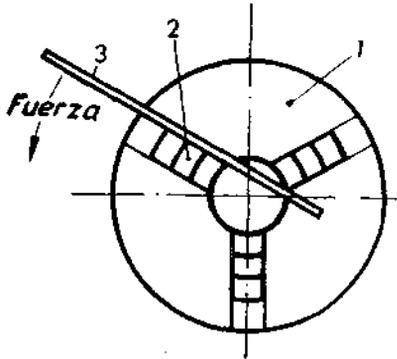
Desmontaje del plato universal. — 1, Plato. — 2, Patas. — 3, Palanca.
